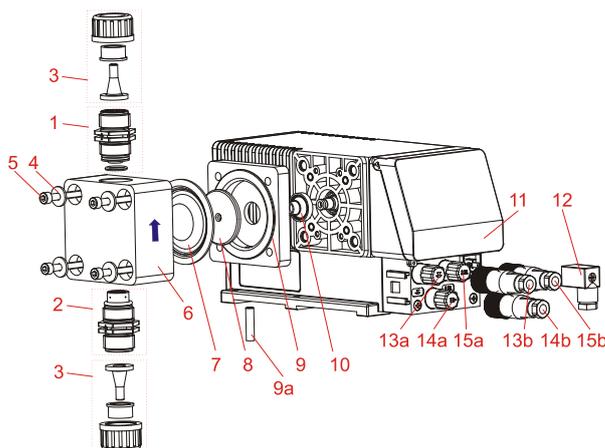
Vue éclatée / Liste des pièces, type 00240
